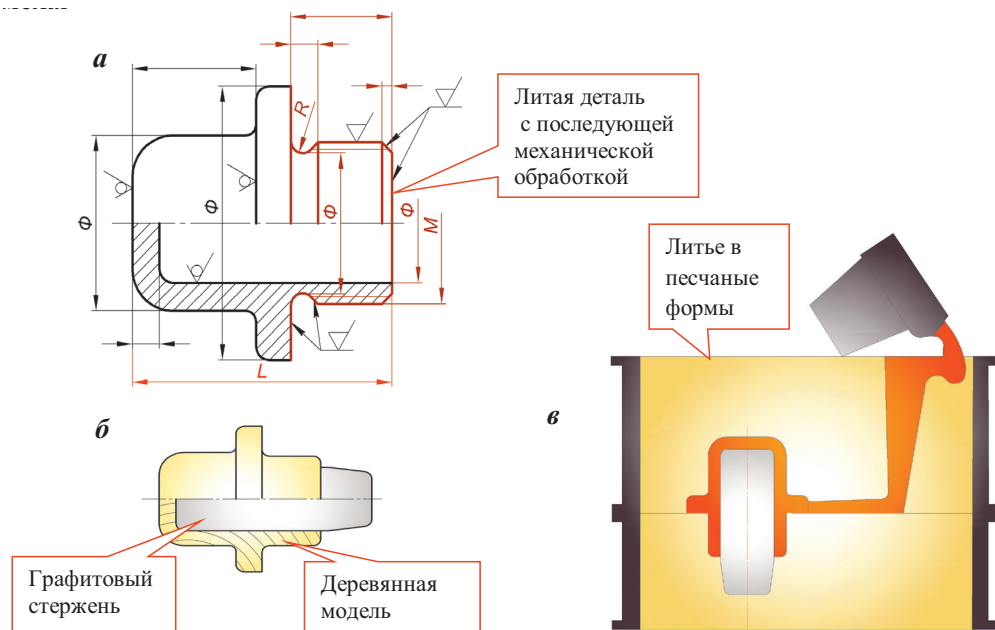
Изготовление детали литьем в песчаные формы с последующей механической обработкой:
